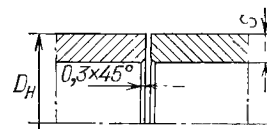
Подготовка кромок стыка под сварку по методу автоопрессовки.
